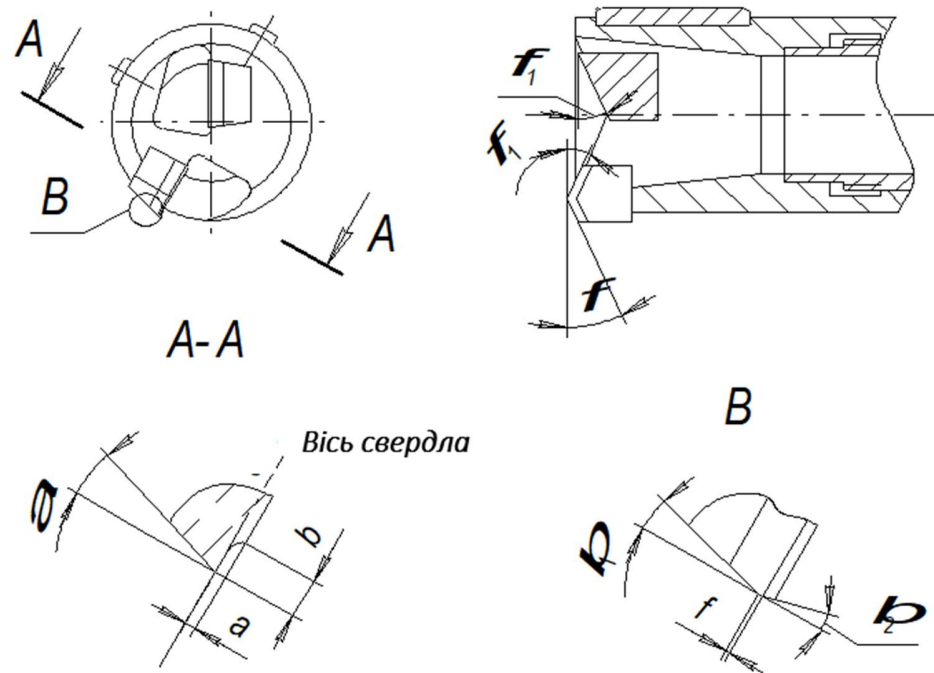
Геометричні параметри різальних крайок свердла для глибокого свердління
